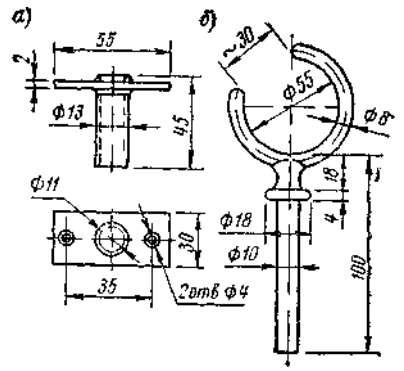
Подушечка (а) и уключина (б) сварной конструкции.
